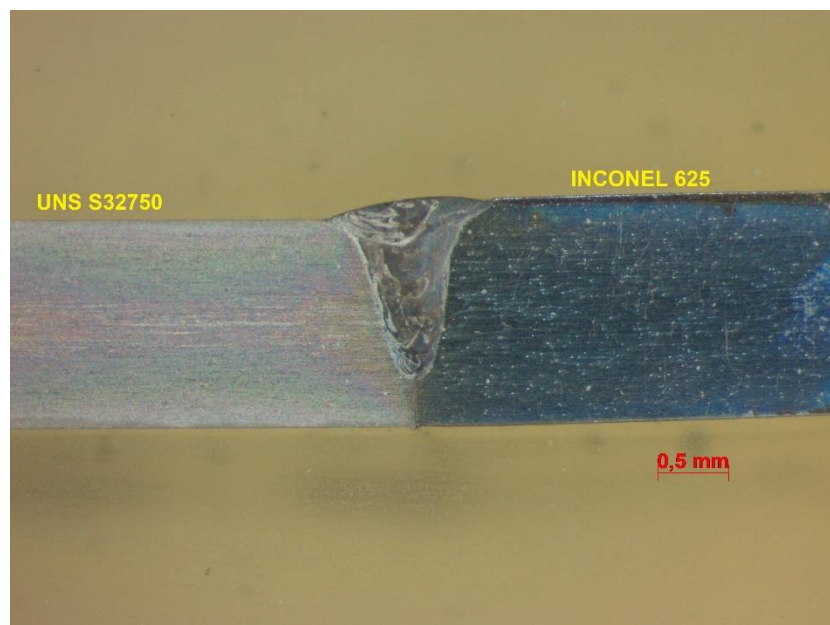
Corpo de prova 2, soldado com frequência 3hz
